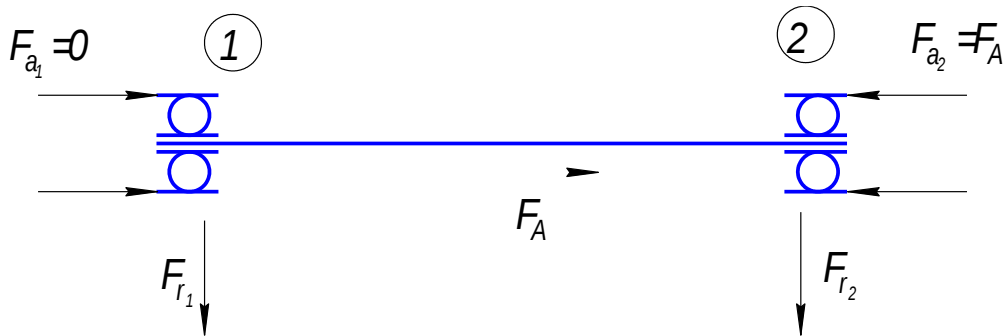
Схема действия нагрузок на подшипники ведомого вала
